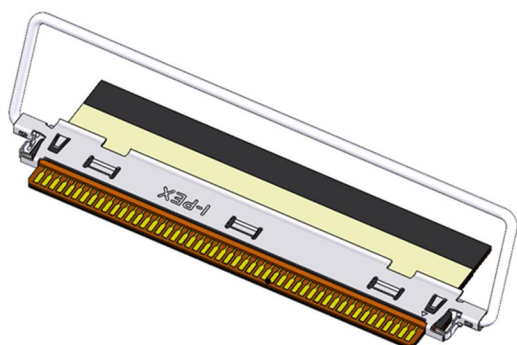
CABLINE-CAL IIF Plug Shell Assembly with FPC
